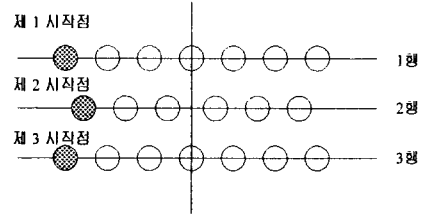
Tube Sheet의 드릴 가공 위치의 배열
